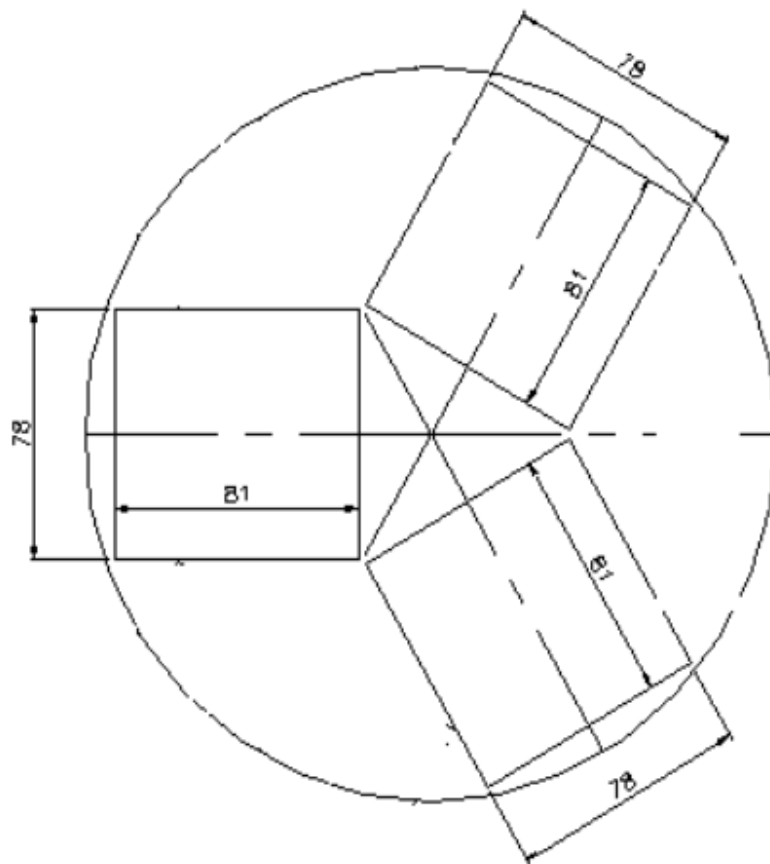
Cortes dos corpos-de-prova CT, na direção CR, dimensões em mm.
